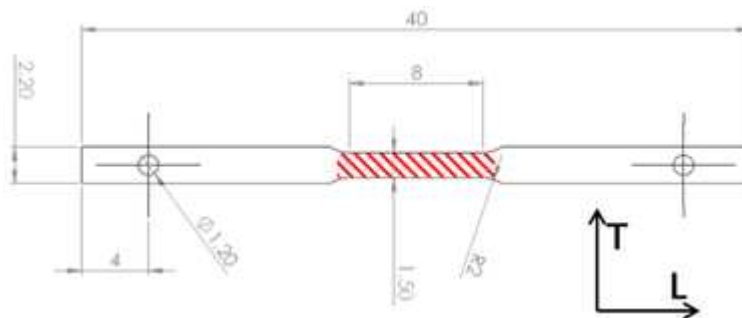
Dimensions des éprouvettes prélevées sur la plaque irradiée. La zone irradiée est délimitée par les hachures rouges.
